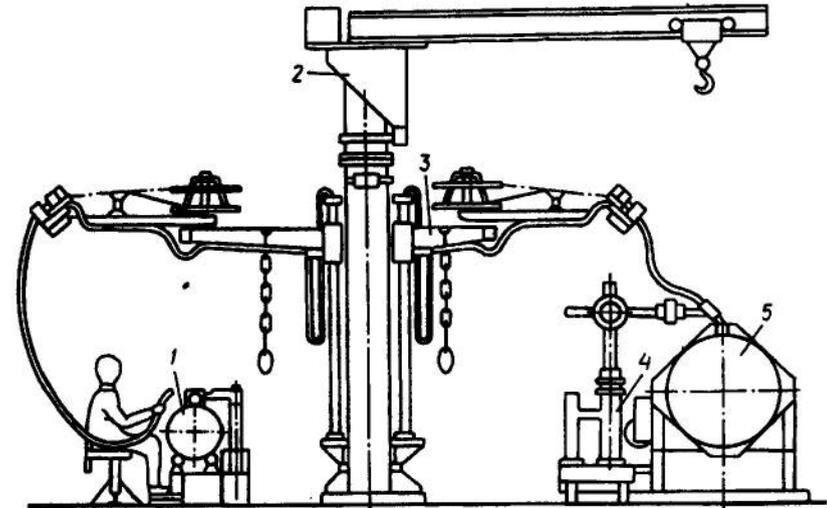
Комплексно-механізована дільниця УД-266 для складання й дугового зварювання циліндричних виробів:
